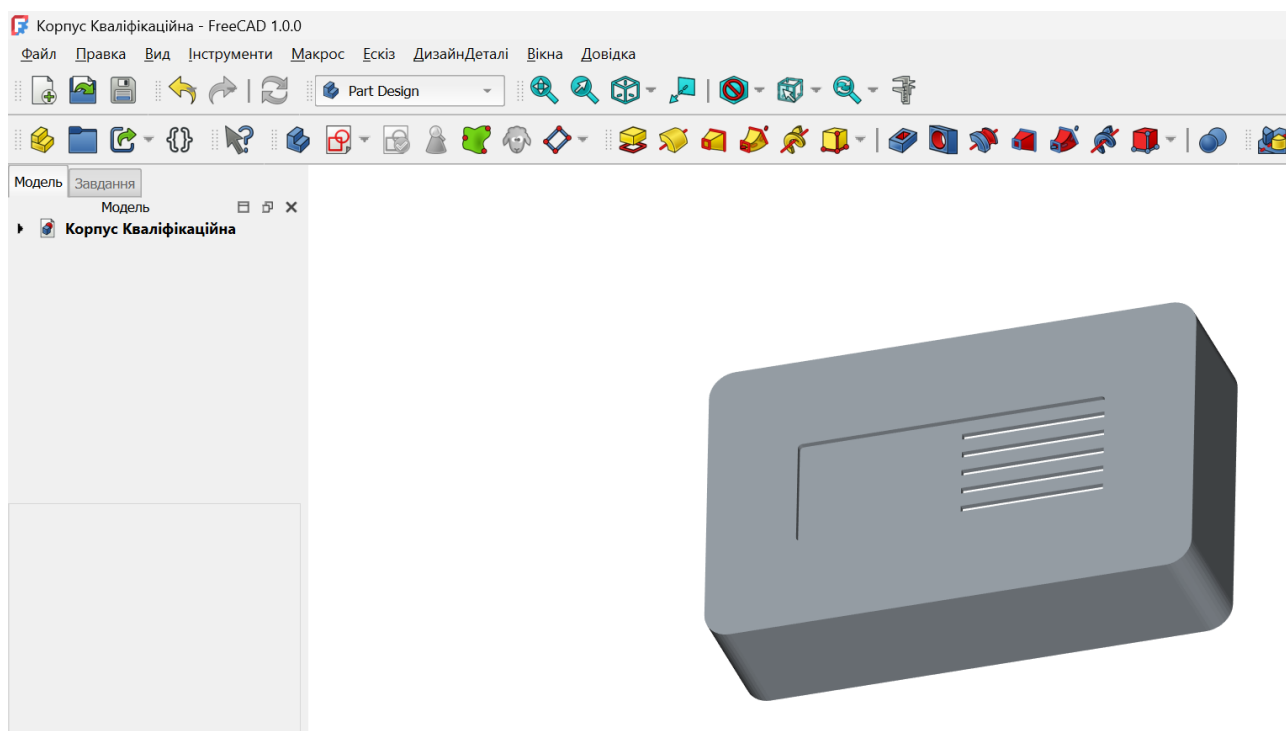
3D-модель корпусу пристрою у середовищі FreeCAD
